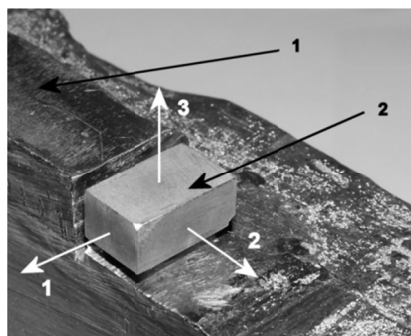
Внешний вид фрагмента стенки корпуса реактора ВВЭР-440: 1 — фрагмент стенки, 2 — образец из наплавленного слоя.
